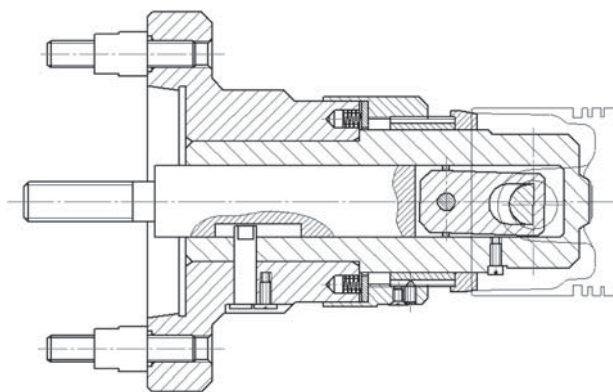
Патрон для полустивовой обработки поршня и прорезания канавок под поршневые кольца
